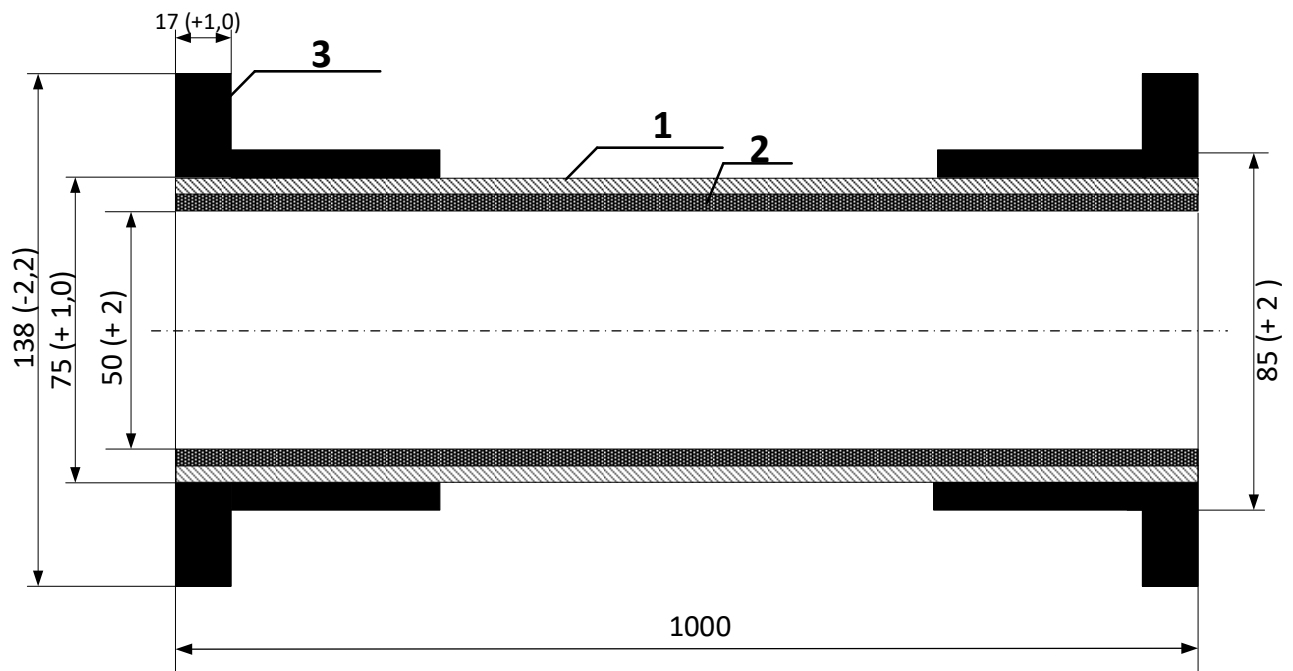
Эскиз образца № 1 (размеры в миллиметрах): 1 – несущий давление полиэтиленовый слой, 2 – слой из TPV, 3 – полиэтиленовая втулка под фланец, приваренная к наружной поверхности трубы
